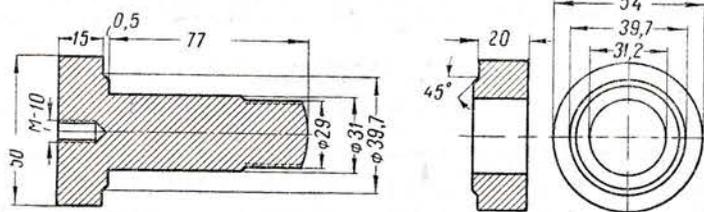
Детали прибора для заливки шатунных подшипников Л-3/2
